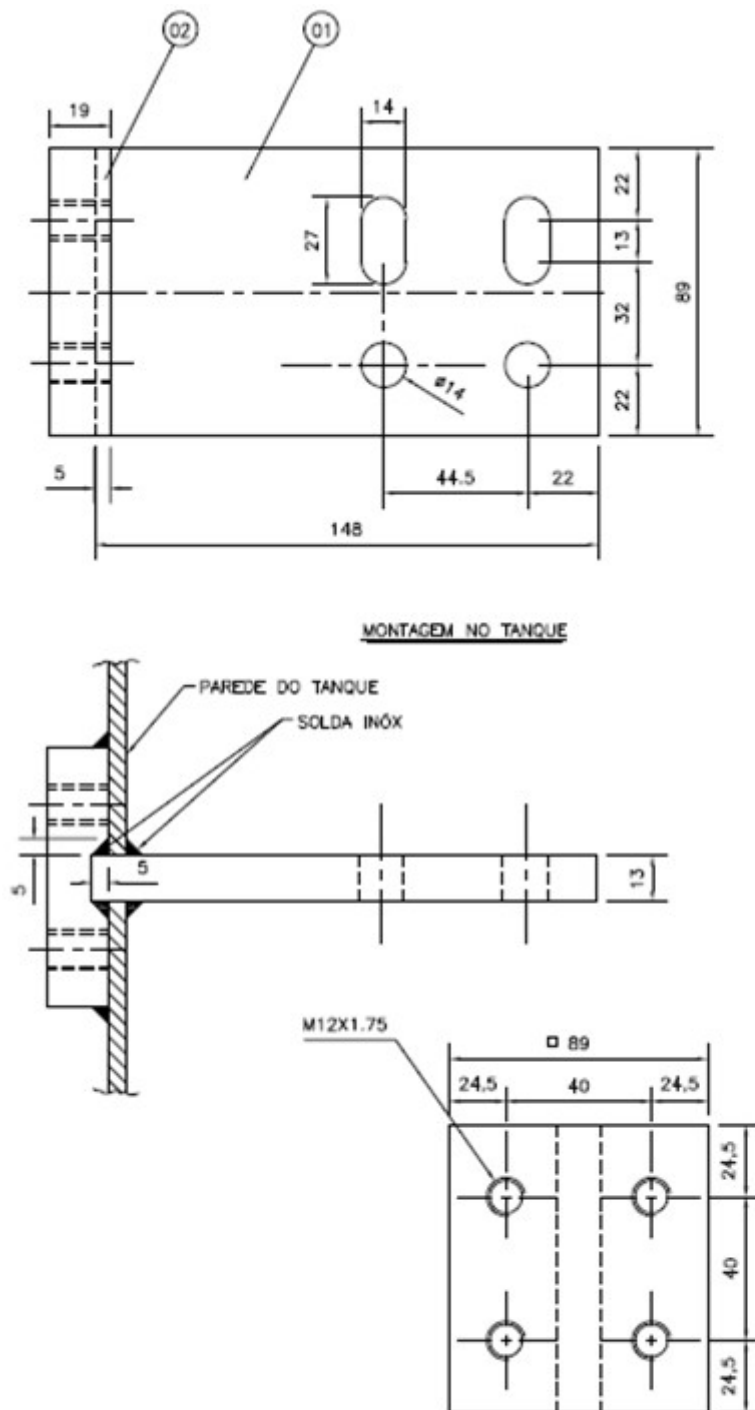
Dimensões (em mm) conector flexível de BT até 1875A
